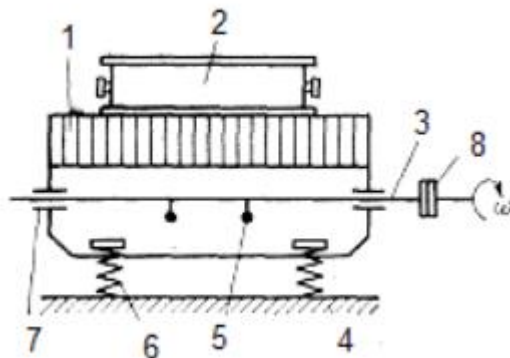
Принципова схема вибивної інерційної решітки [1]
